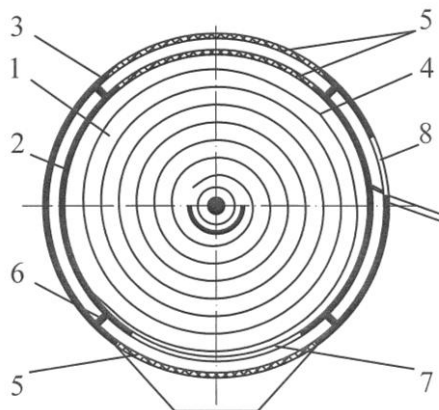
Сушарка з спіралеподібною поверхнею: 1 – сушильна камера; 2 – циліндрична обичайка; 3 – кожух; 4 – спіралеподібна поверхня; 5 – перфоровані вставки; 6 – поличка; 7 – вікно для вивантаження матеріалу; 8 – вивантажувальний отвір
